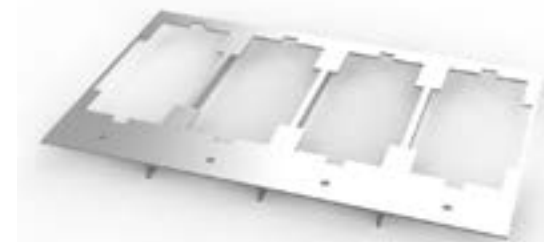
Estrutura metálica para a integração de 4 elementos para colocação na categoria estrutura
